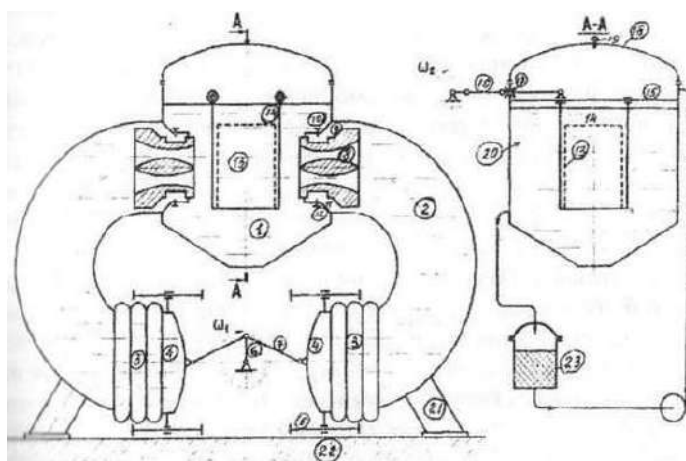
Схема моечной установки для очистки корпусных деталей:
